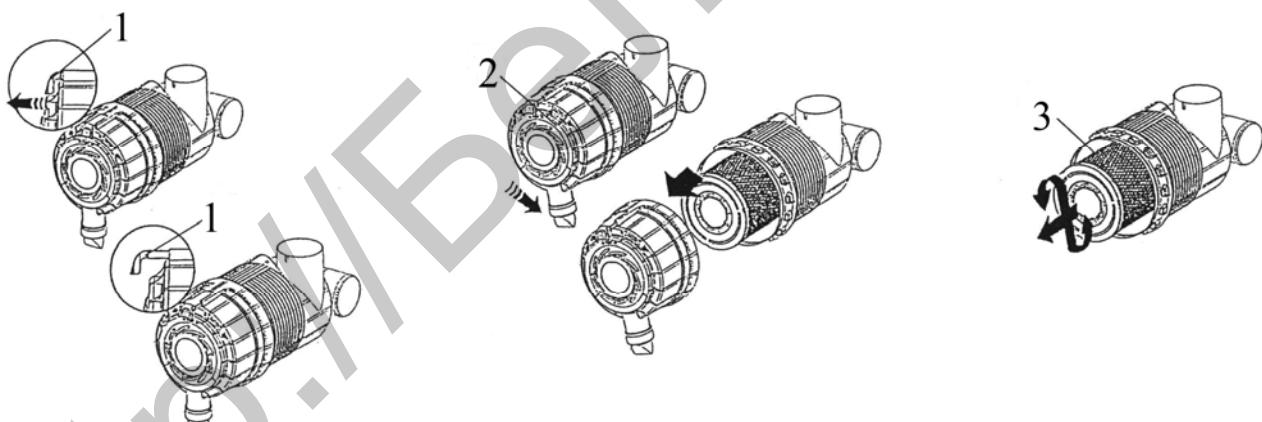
Проверка воздухоочистителя дизеля
